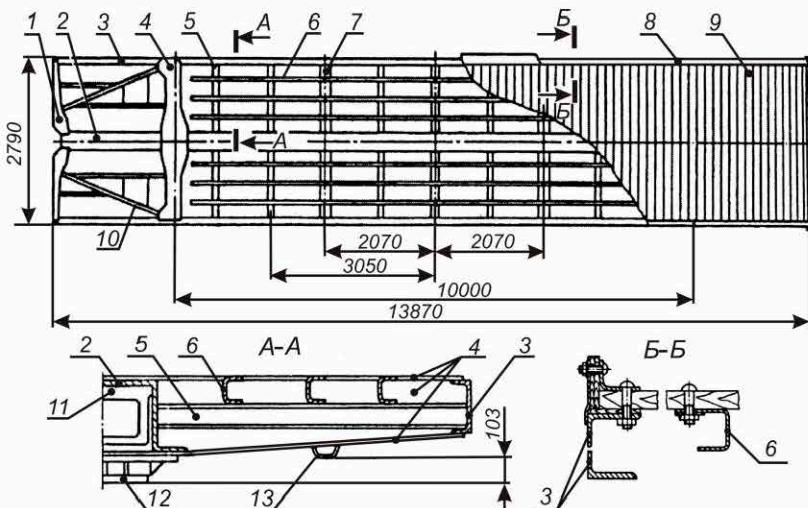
Рама с полом универсального крытого вагона модели 11-217
